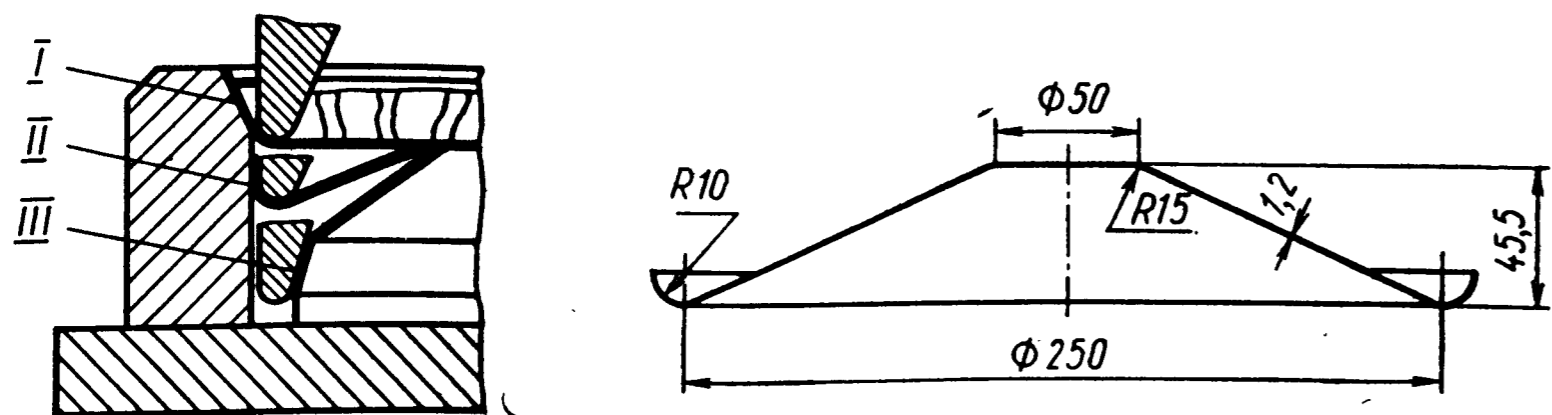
Последовательность вытяжки конической детали на штампе для реверсивной вытяжки
